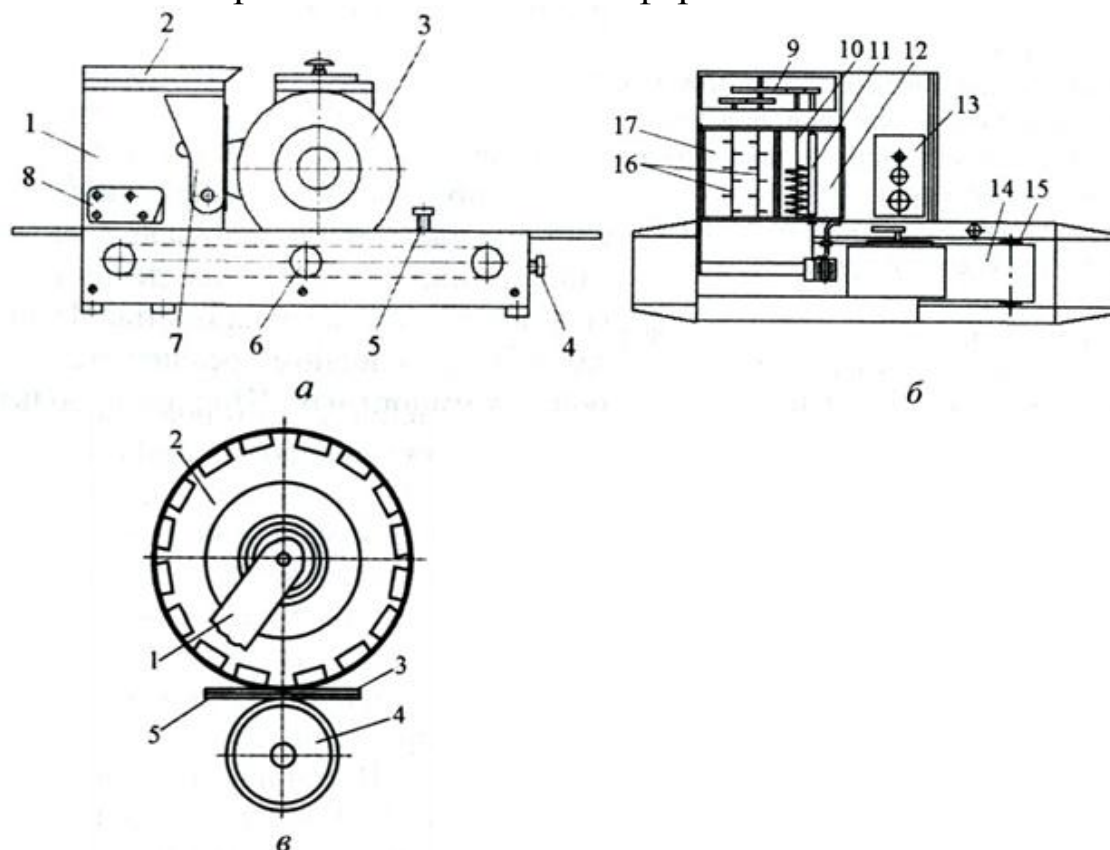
Агрегат для приготовления пельменей и вареников Л5-ФАП:
